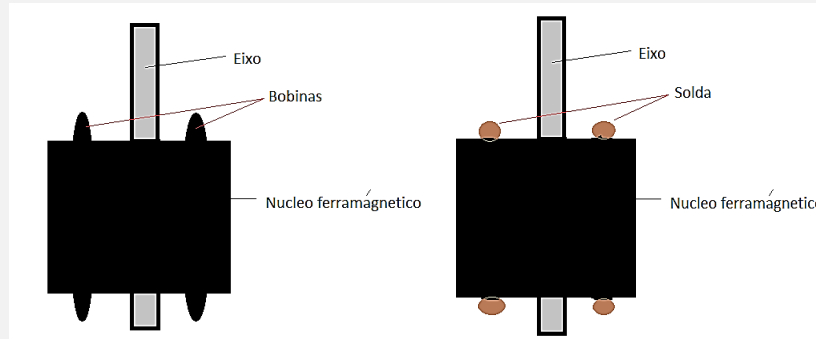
Rotor bobinado de um motor de corrente alternada (Esquerdo), Rotor bobinado transformado em gaiola (direito) Fonte: [Autor]
